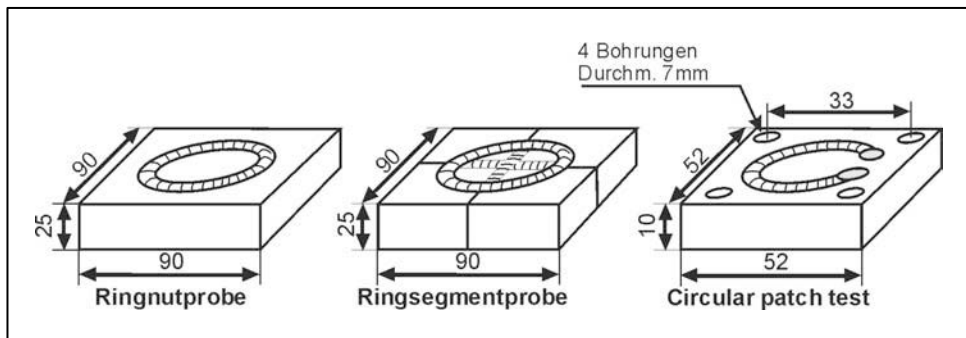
Ringnutprobe, Ringsegmentprobe [112], Circular Patch Probe [113]
